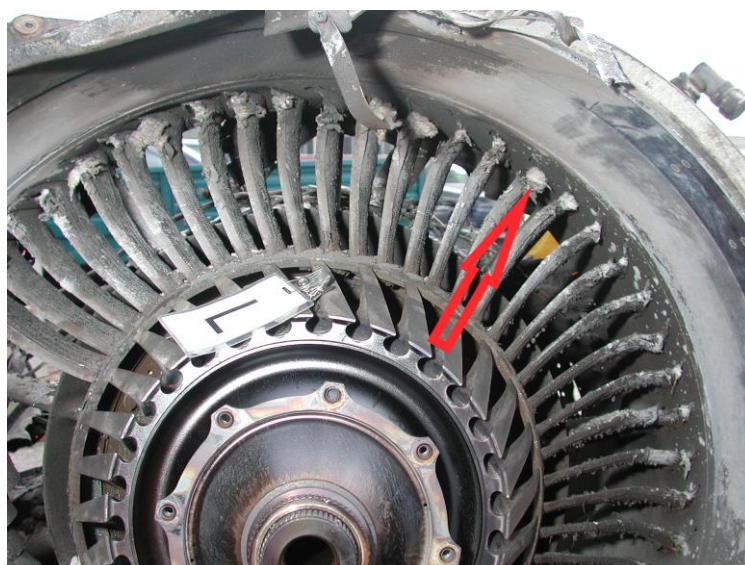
particolare dei residui organici prelevati dalle palette statoriche del fan sinistro.
